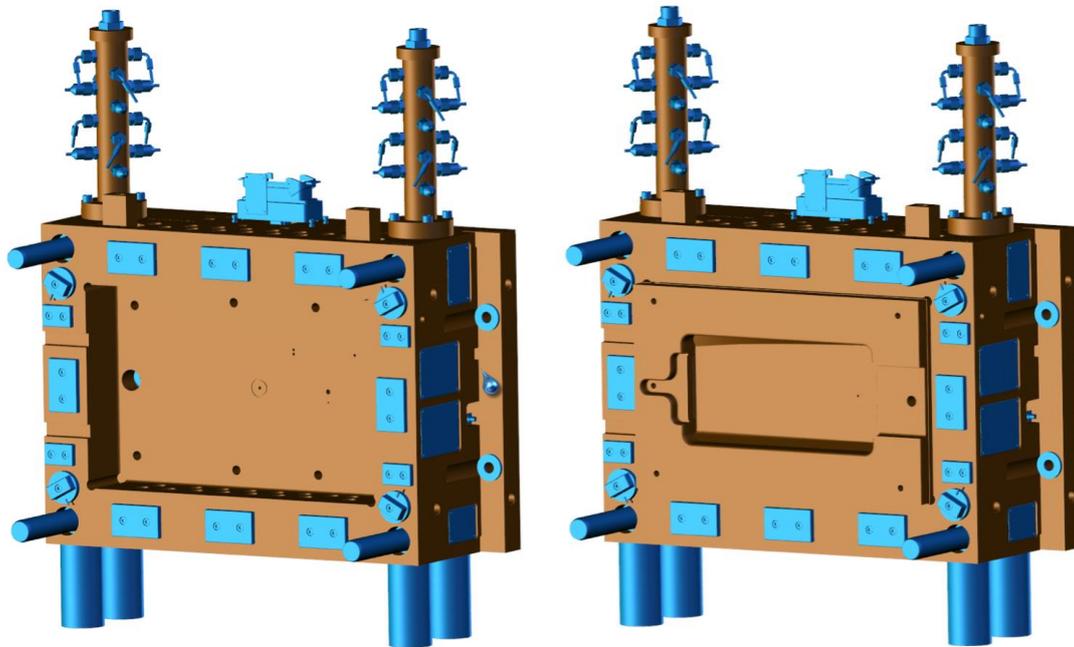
Aufbau des Chassis-Werkzeugs ohne Einsatz (links) und mit eingebautem 2K-Plattenwerkzeug (rechts)
